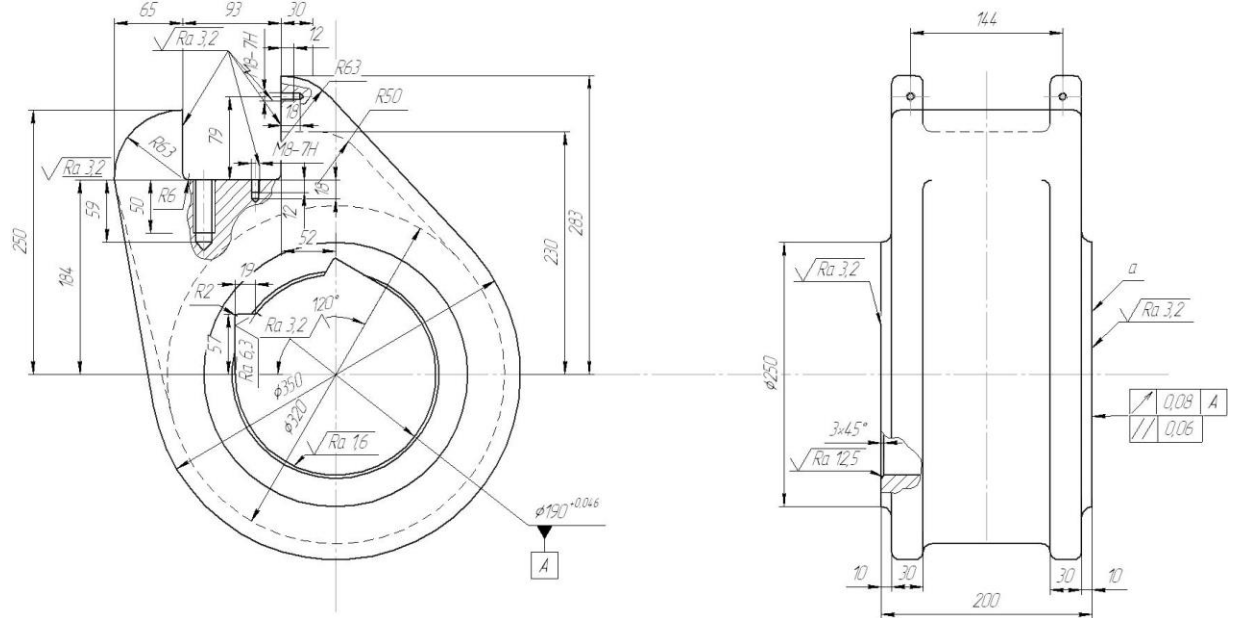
Відхилення форми та розташування поверхні деталі
